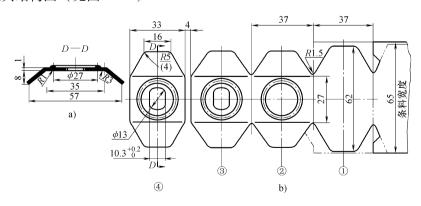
碟形弹簧级进模 a) 零件图 b) 排样图
